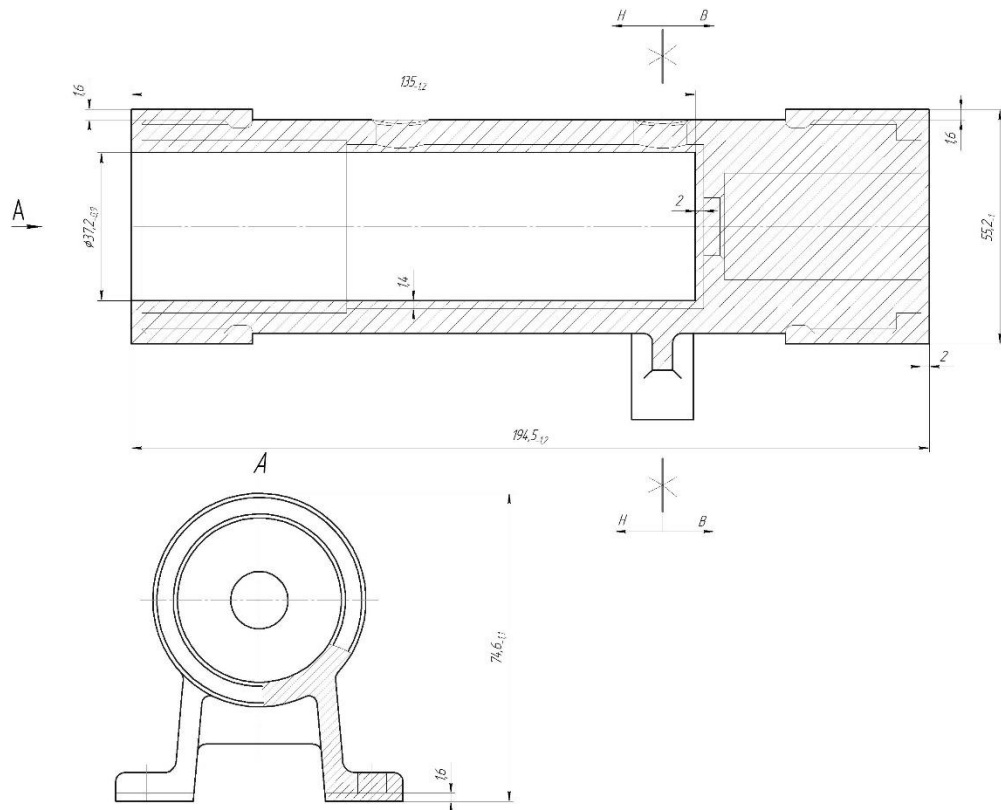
Ескіз заготовки з припусками отриманими литтям в піщані форми з машинною формовкою
